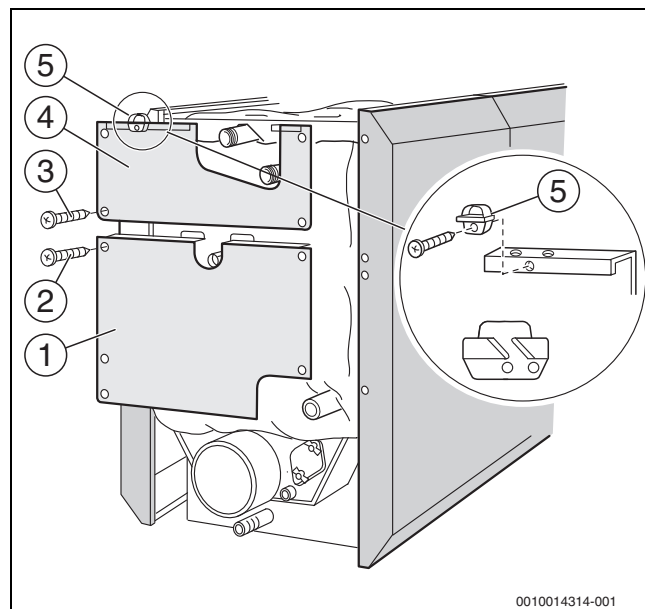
Fixați cu șuruburi peretele posterior compus din 2 elemente
